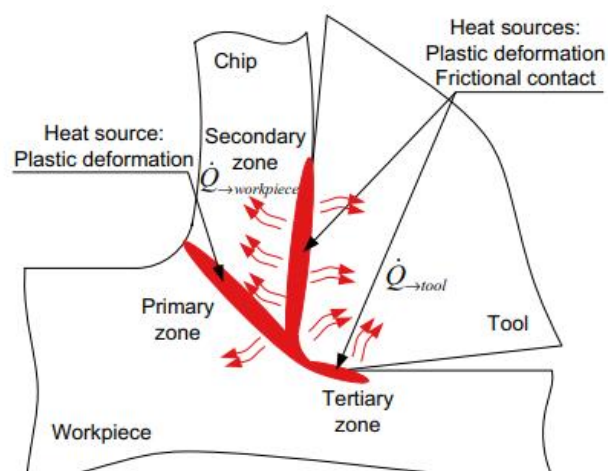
Основні джерела тепла під час формування стружки при механічній обробці [29].
